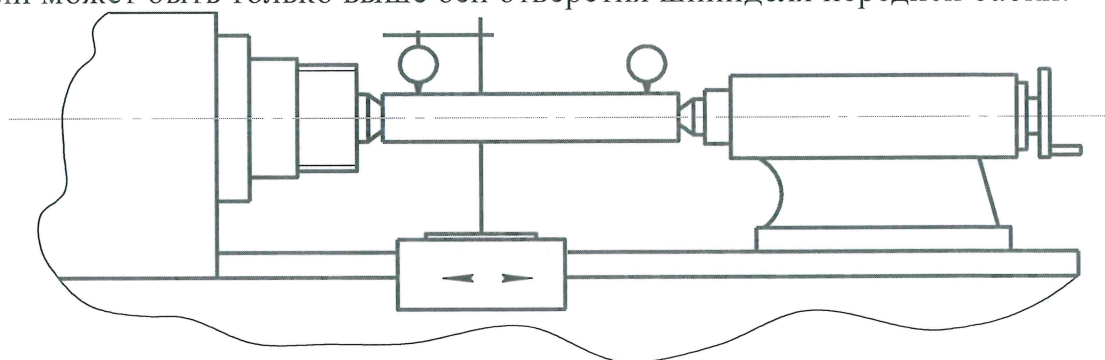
Схема установки индикатора для проверки расположения осей отверстия шпинделя передней бабки и пиноли на одинаковой высоте над направляющими станины и суппорта
